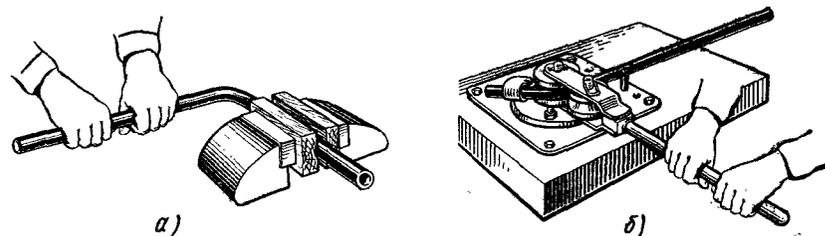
Гибка труб из цветных металлов: а — в тисках; б — в роликовом приспособлении
